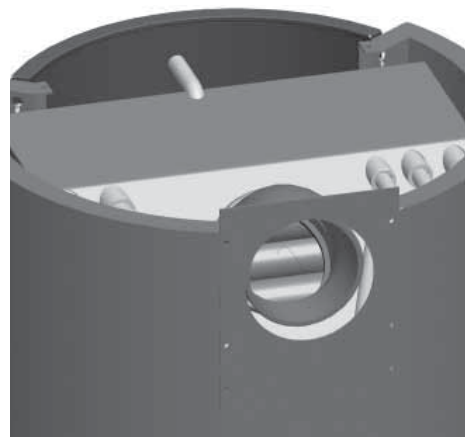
Gewindemuffen für Entlüfter, TAS- und Kesselfühler
